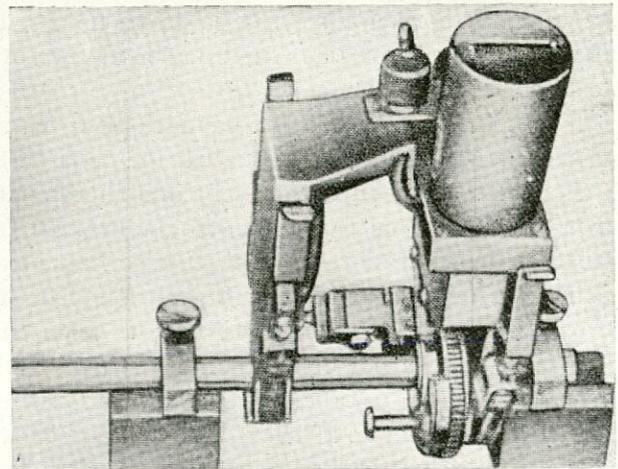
Equipo para soldadura eléctrica de tubos en atmósfera de argón.
